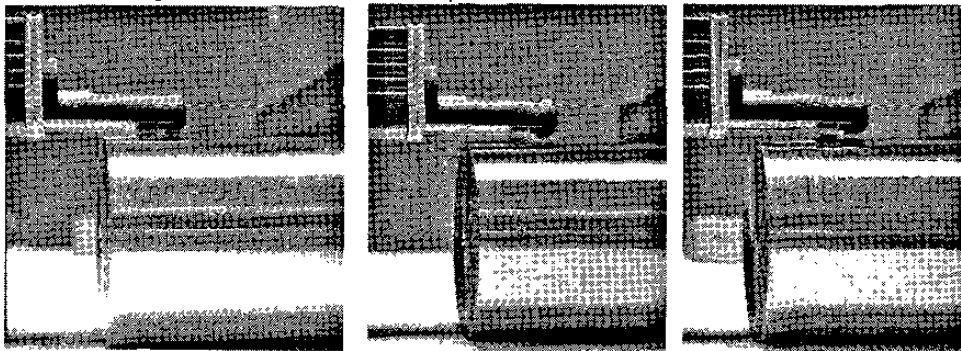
Palpador del rugosímetro sobre cada pieza maquinada
